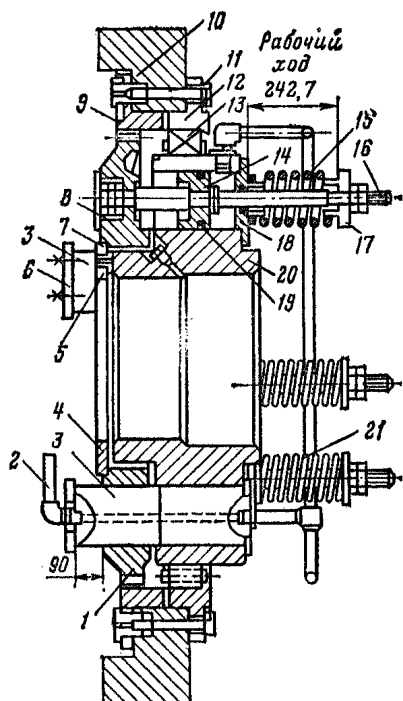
Зубчатый безрычажный механизм перестановки завода ЛКУ с пневматическим приводом
